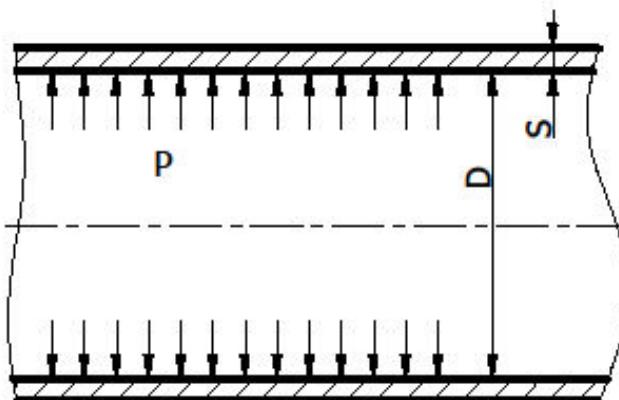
Розрахункова схема циліндричної обичайки
